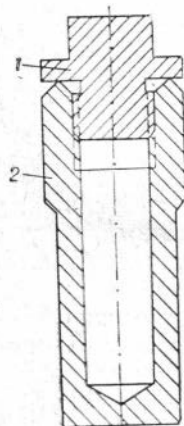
Вкладыш: 1 — пробка; 2 — корпус.
